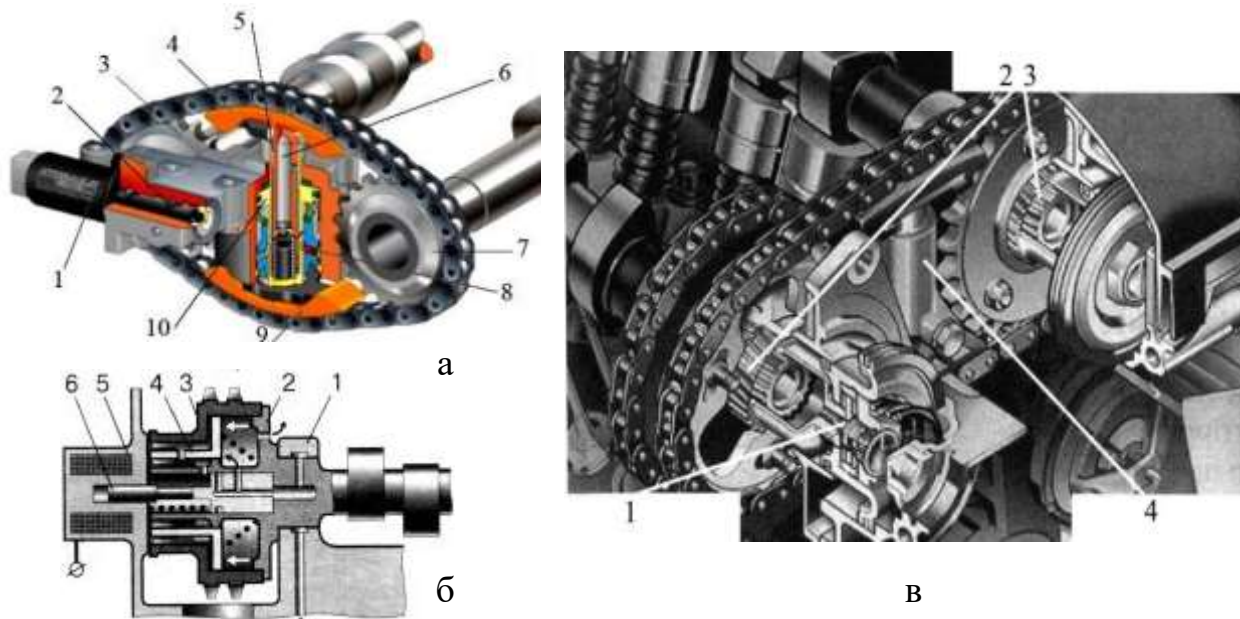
Пристрої для зміни фаз газорозподілу: а – з натягом ланцюга: 1 – керуючий клапан; 2 – золотник; 3 – зірочка приводу впускних клапанів; 4, 9 – натяжители ланцюга; 5 – штовхач натяжителя; 6 – порожнина для масла; 7 – зірочка приводу випускних клапанів; 8 – фіксатор стартовий; 10 – керуючий поршень; б – з поршневым приводом: 1 – головка блоку; 2 – розподільний вал; 3 – зірочка приводу РВ; 4 – поршень; 5 – обмотка електромагніту; 6 – якір-клапан; в – поєднана система: 1 – керуючий поршень; 2 – косозуба шестерня; 3 – прямозуба шестерня; 4 – натяжитель ланцюга
